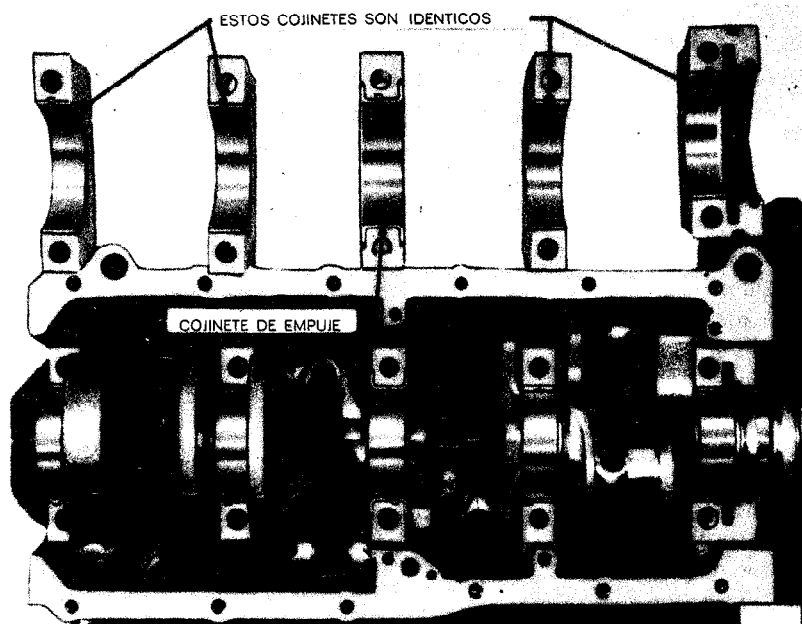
Disposición de los cojinetes de bancada en un motor V-8. Los sombreretes con sus cojinetes se han separado de su lugar y situado encima del motor (parte superior de la figura). El cojinete central es un cojinete de empuje (Buick Motor Division of General Motors Corporation).
